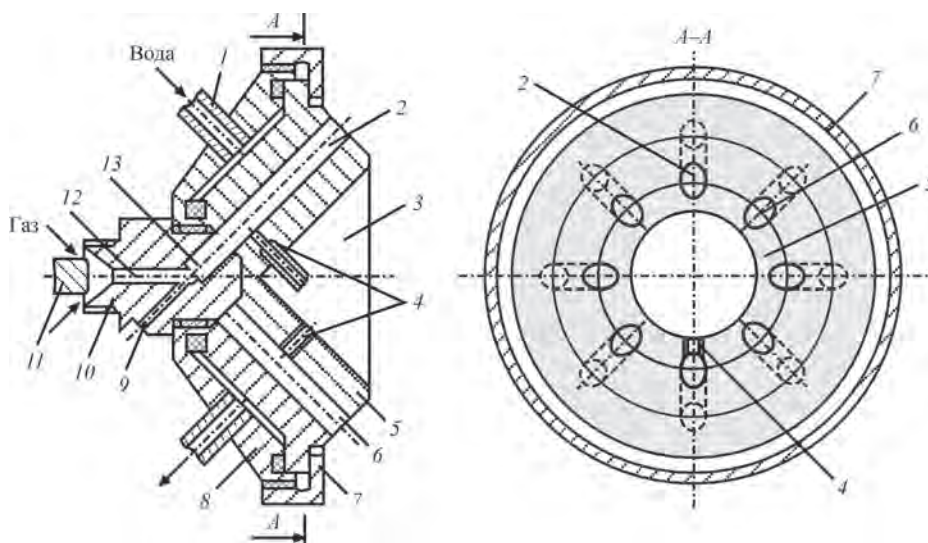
Конструкція генератора плазми для нанесення багатокомпонентних покриттів: 1 – штуцер; 2 – кінцева ділянка вихідної частини дугового каналу; 3 – порожнина; 4, 9 – канали подавання порошку; 5 – вихідна частина аноду; 6 – ділянки дугового каналу; 7 – накидна гайка; 8 – корпусна деталь; 10 – вхідна частина аноду; 11 – катод; 12 – вхідна частина дугового каналу; 13 – початкова ділянка вихідної частини дугового каналу
